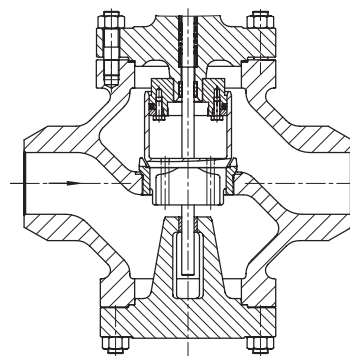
· Vanne type 3254 avec embouts à souder et clapet équilibré
